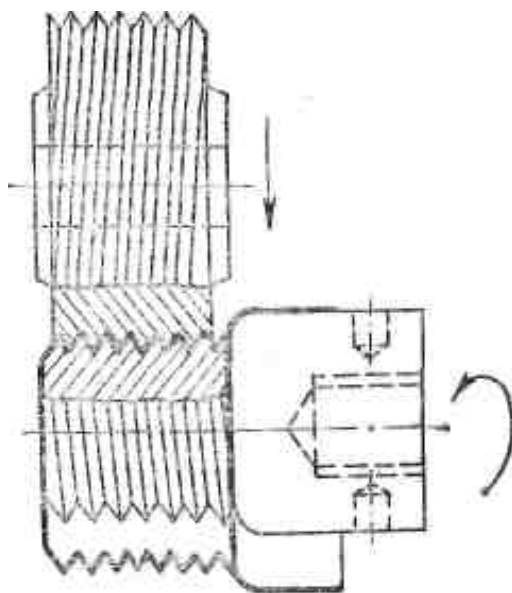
Накатка резьбы при помощи патрона и ролика
